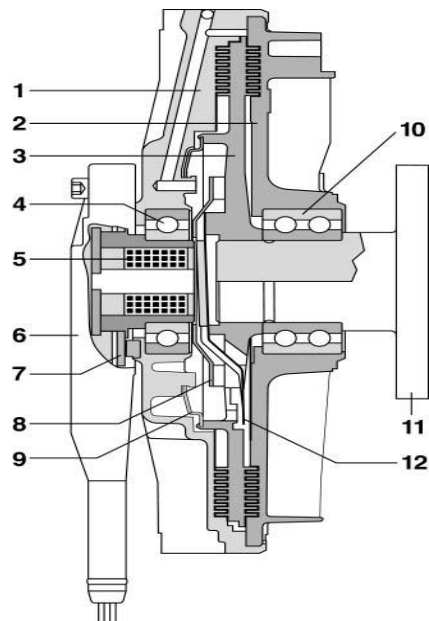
Ventilador com atuador eletromagnético; 1- Corpo básico, 2 – Capa, 3- Disco primário, 4- Flange eletromagnética, 5- Bobina, 6- Solenóide, 7 - Ímã permanente, 8- Embreagem, 9 - Disco intermediário, 10 - Rolamento de acoplamento, 11 - Eixo com Flange, 12- Válvula.
